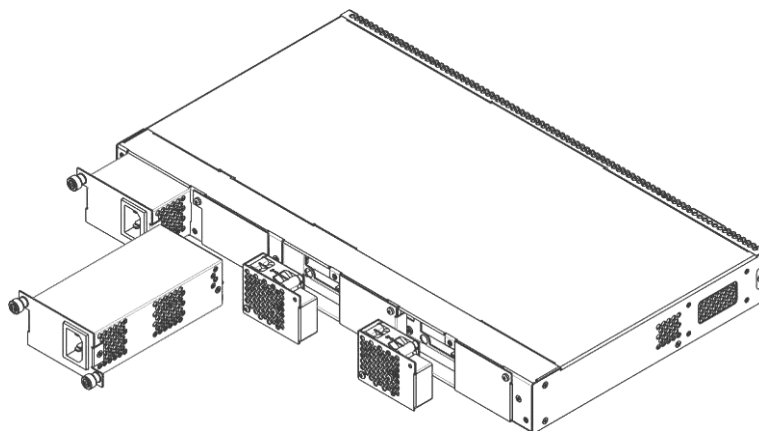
Блок вентиляции SMG-1016M. Крепление в корпус
